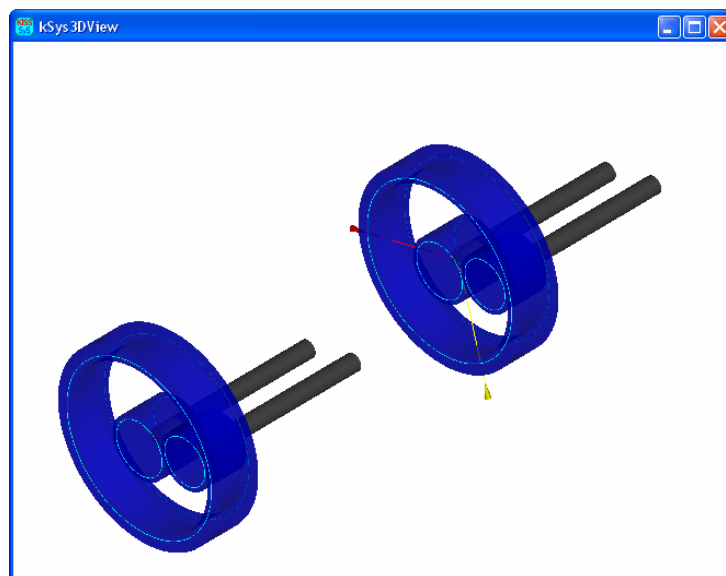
3D Ansicht mit Hohlräder.
